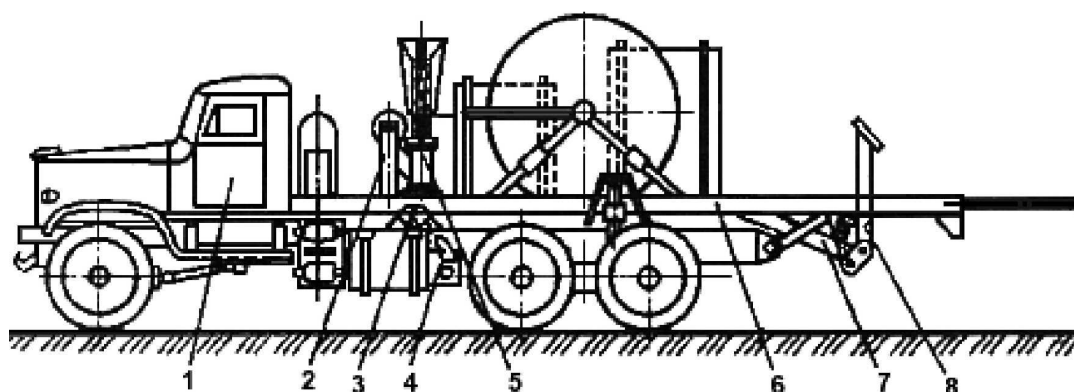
Агрегат АТЭ-6 для установок ЭЦН:
